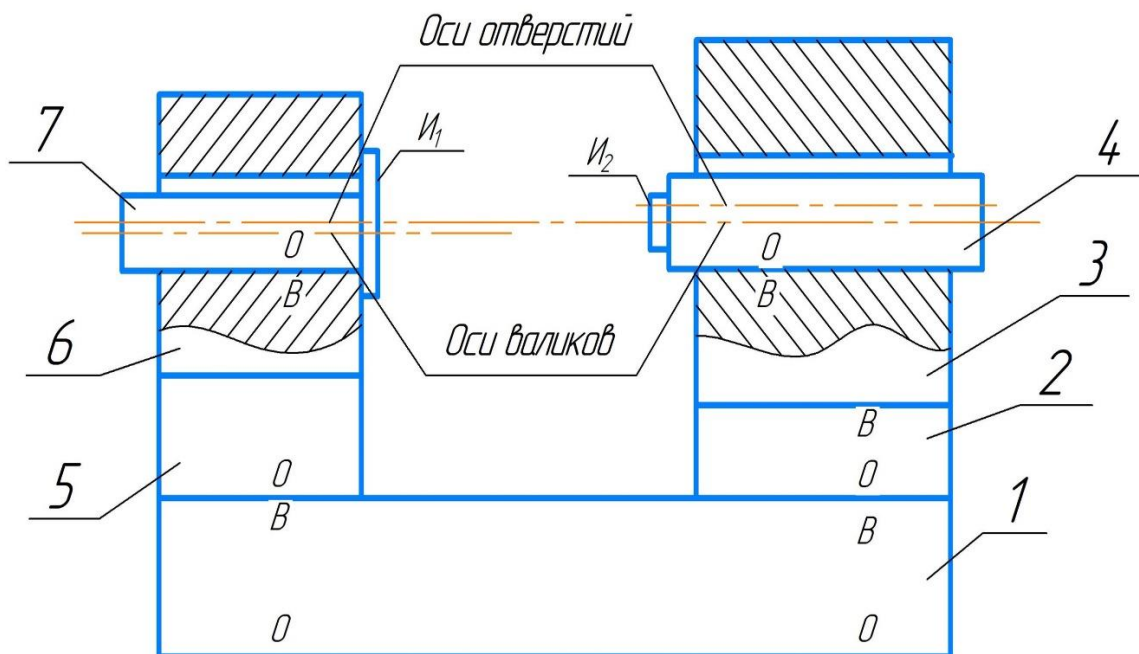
Схема соединения деталей и сборочных единиц при построении машины.
